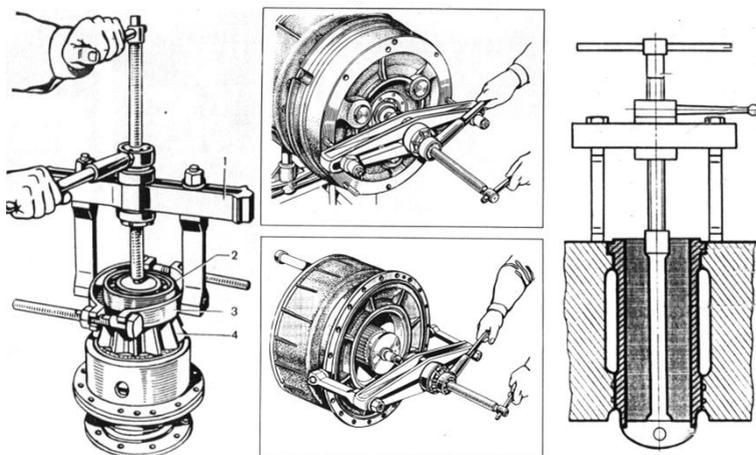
Варианты применения съёмника со сменной оснасткой: 1 – съёмник; 2 – подшипник; 3 – обойма; 4 – шестерня главной передачи
